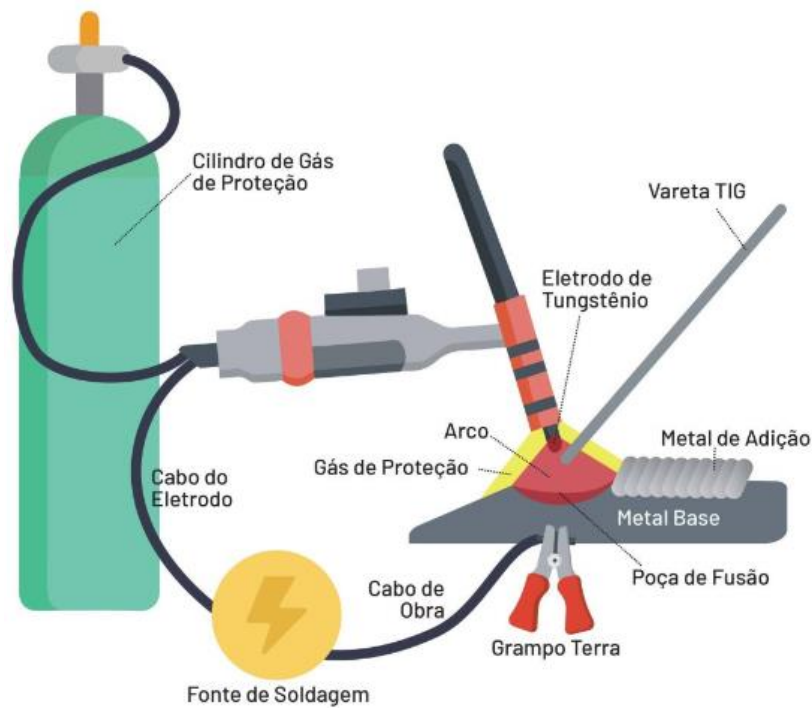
Desenho representativo da soldadura TIG (GTAW) [25].
